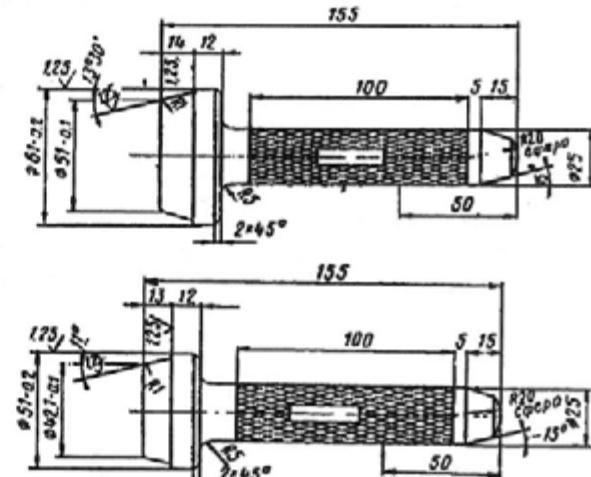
Оправка для запрессовки наружных колец подшипников в ступицу колеса:
